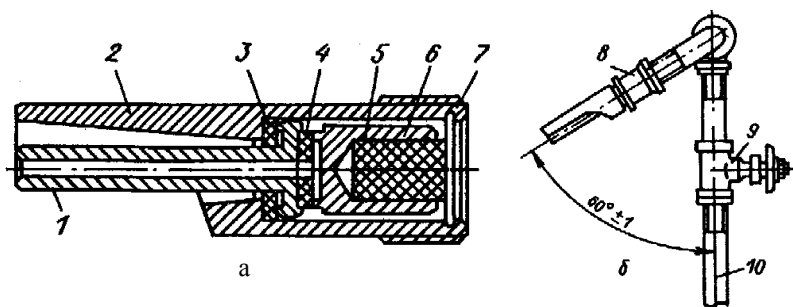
Соскова безчашечна автоматична напувалка ПБС-1 для свиней: а-будова напувалки; б-схема її встановлення; 1-сосок; 2-корпус; 3, 4-ущільнюючі прокладки; 5-амортизатор; 6-клапан; 7- упор; 8-муфта; 9-вентиль; 10-стояк.
